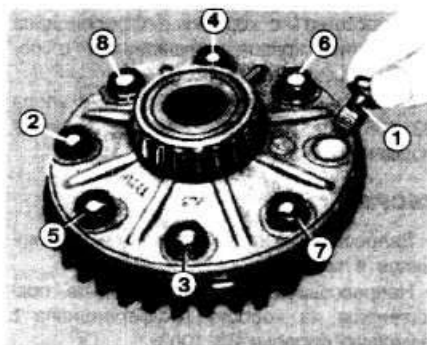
Порядок затяжки болтов крепления ведомой шестерни главной передачи к коробке дифференциала
